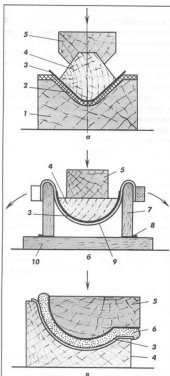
Облицовывание криволинейных поверхностей в приспособлениях:
